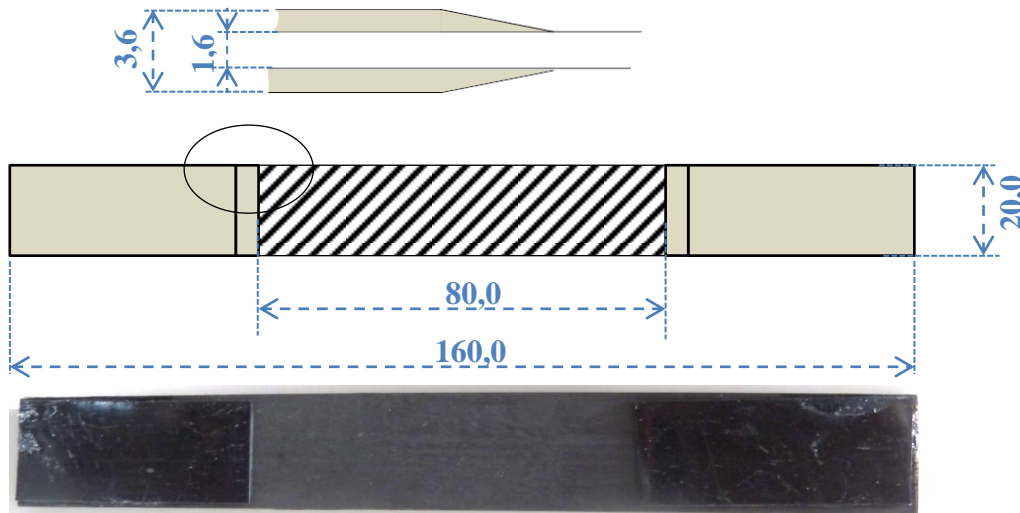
Dimensions et forme de l'éprouvette de stratifié  $[\theta]_8$
